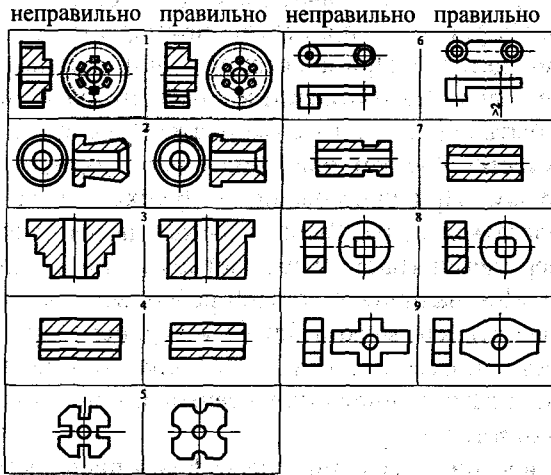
Примеры конструирования металлокерамических заготовок
